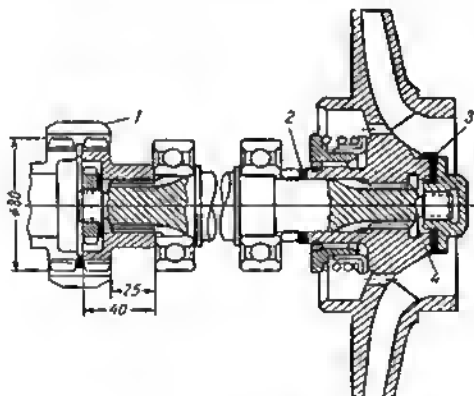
Árbol en conjunto con el rotor de álabes y cojinetes (dibujo de composición)
